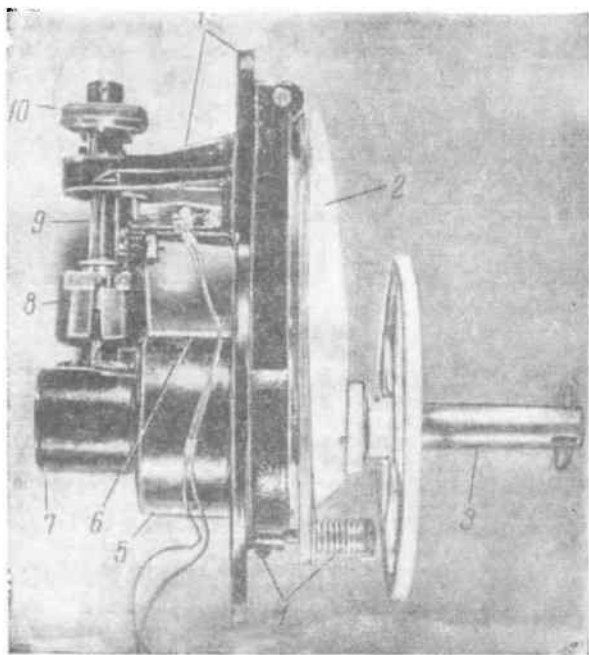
Общий вид наматывателя КП-15А и КП-30:
